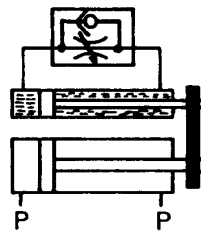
Druckluft-zylinder mit Ölbremsszylinder
